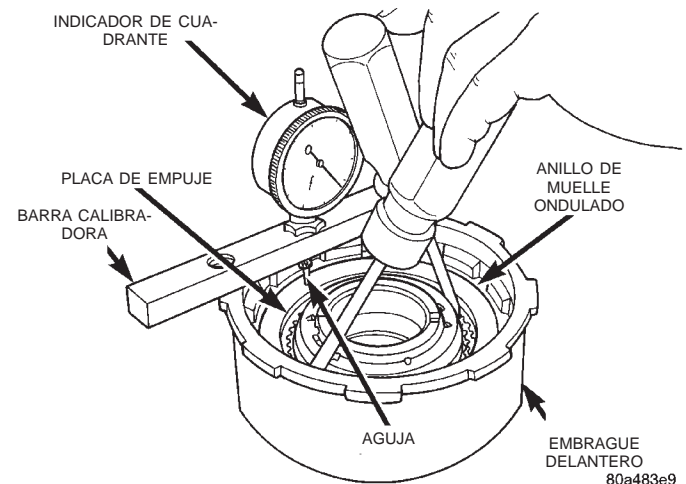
Medición de la holgura del conjunto del embrague delantero
